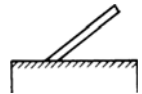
Rutscherstein. Der Stahl wird diagonal zur Fasse bewegt. Sattes Auflegen beachten.
